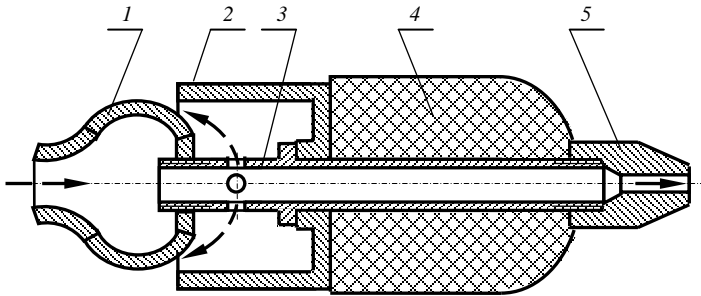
Гидрореактивный снаряд: 1 – сферическая камера; 2 – камера реакции; 3 – осевой патрубкок; 4 – деревянный кожух; 5 – сопло
